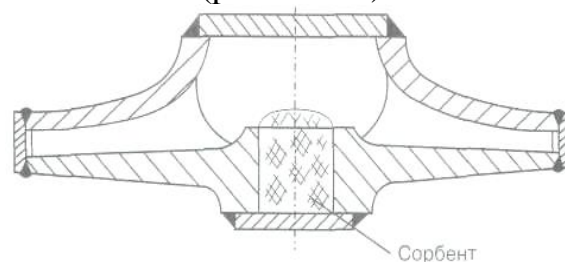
Схема підготовки робочого колеса до термообробки при автовакуумному нагріванні
